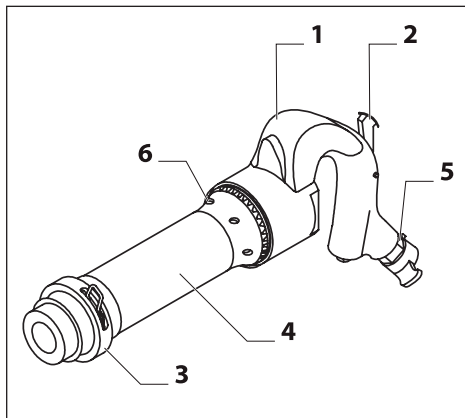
Молоток пневматический отбойный легкий СРН-7
